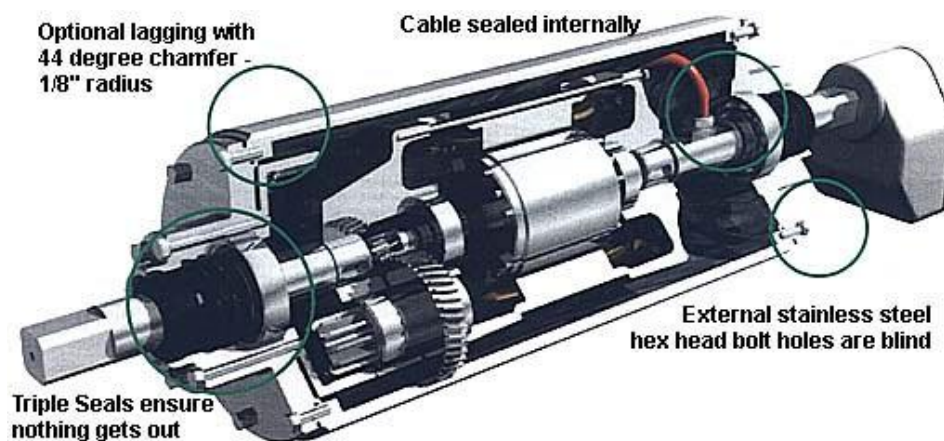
MOTOTAMBOR DRUM MOTOR DETALLE INTERNO
